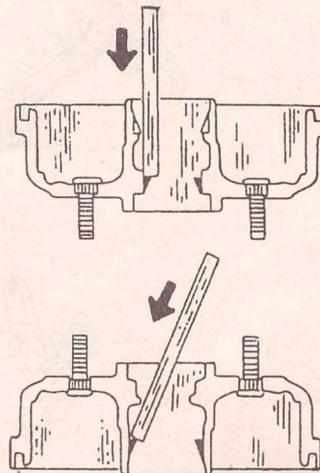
Демонтаж наружных обойм подшипников с противоположных сторон тормозного барабана.
